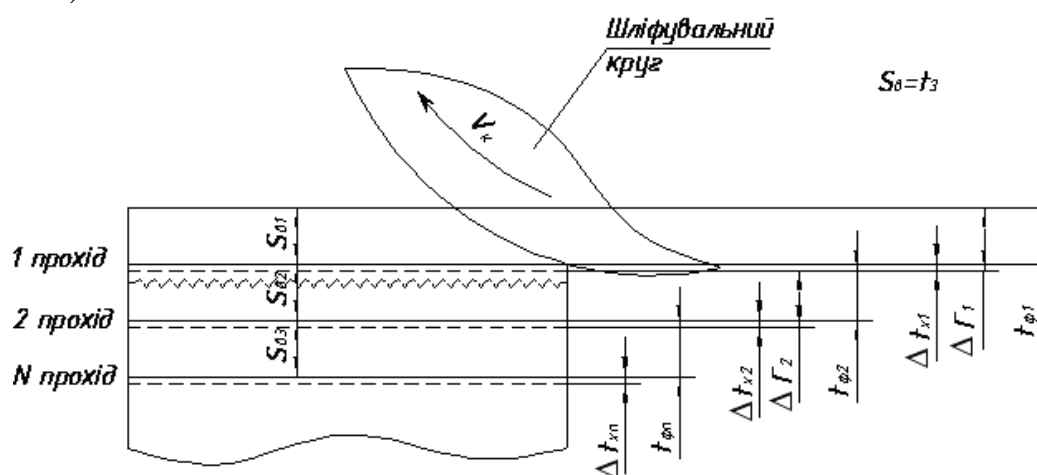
Зняття матеріалу при обробці пористих поверхонь
